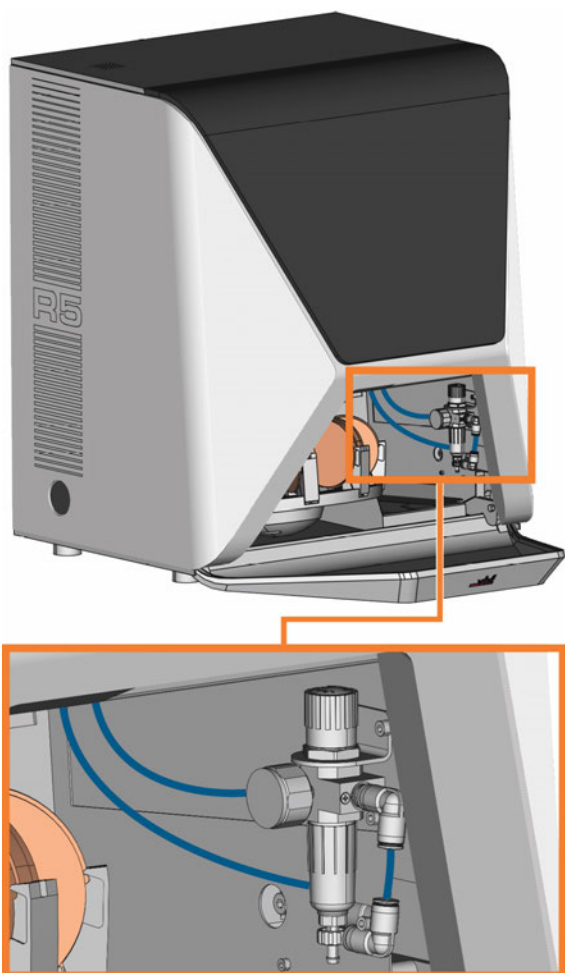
L'EMPLACEMENT DU RÉGULATEUR D'AIR COMPRIMÉ
